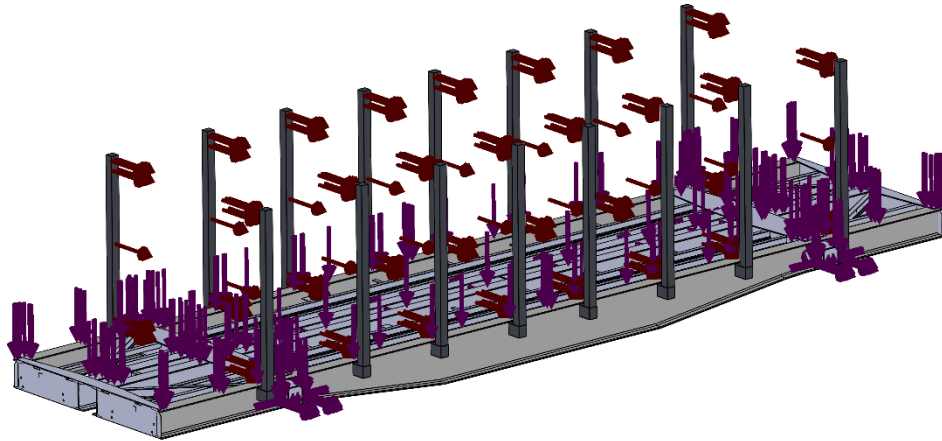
Розрахункова схема несучої конструкції вагона-платформи
